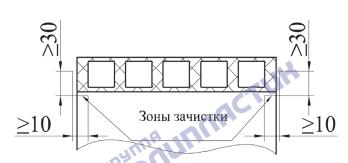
Механическая подготовка свариваемых поверхностей муфты
